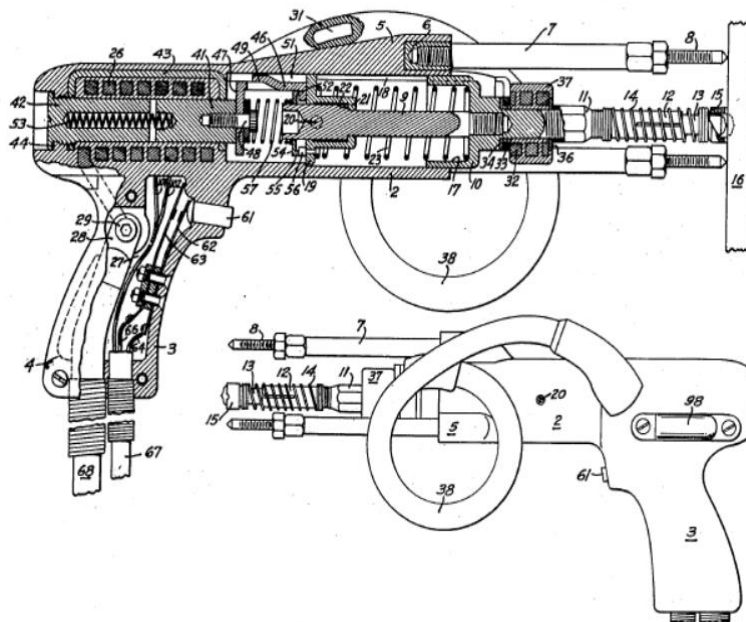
Projeto Ted Nelson - Pistola para soldagem de pinos
